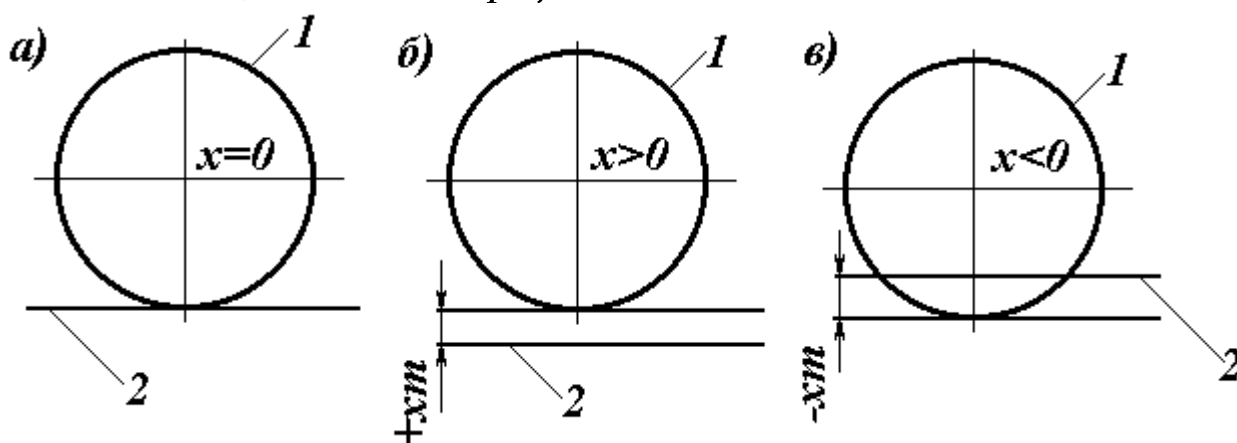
Варианты установок инструмента при нарезании колеса:
